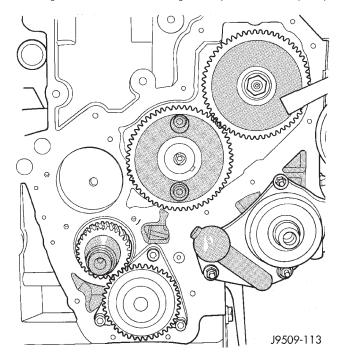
Orifício de Montagem da Bomba a Vácuo
